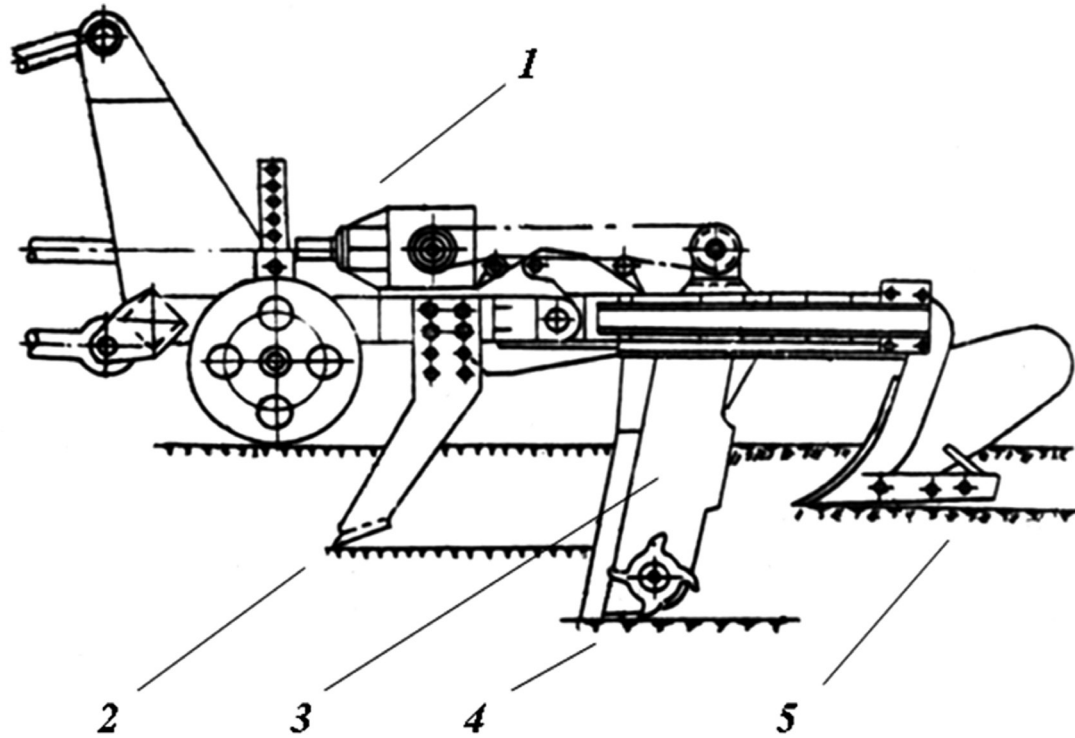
Устройство для мелиоративной внутрипочвенной фрезерной обработки почвы ПМС-70, вид сбоку.
